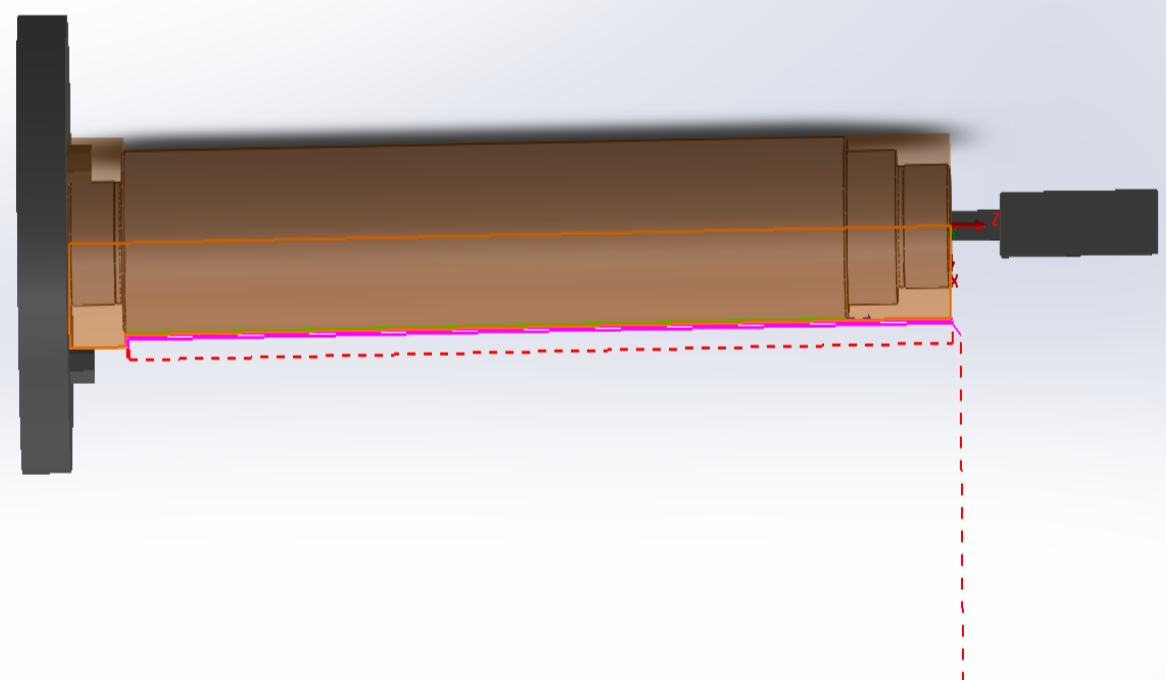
Чорнова та чистова обробка поверхні $\varnothing 52h14$
